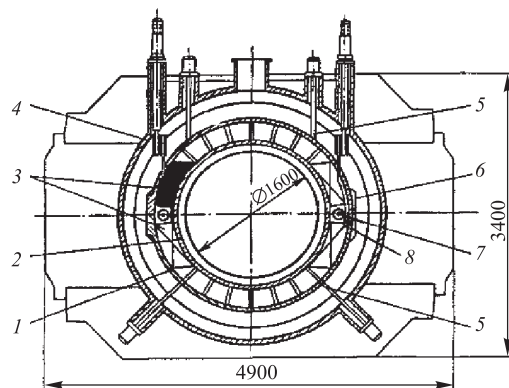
Дипольный магнит с седлообразной цилиндрической обмоткой [24]: 1 — бандажные полуцилиндры; 2 — внутренняя обечайка; 3 — обмотки; 4 — наружная обечайка вакуумного кожуха; 5 — подвеска; 6 — стяжные болты; 7 — титановые тяги; 8 — подвеска
